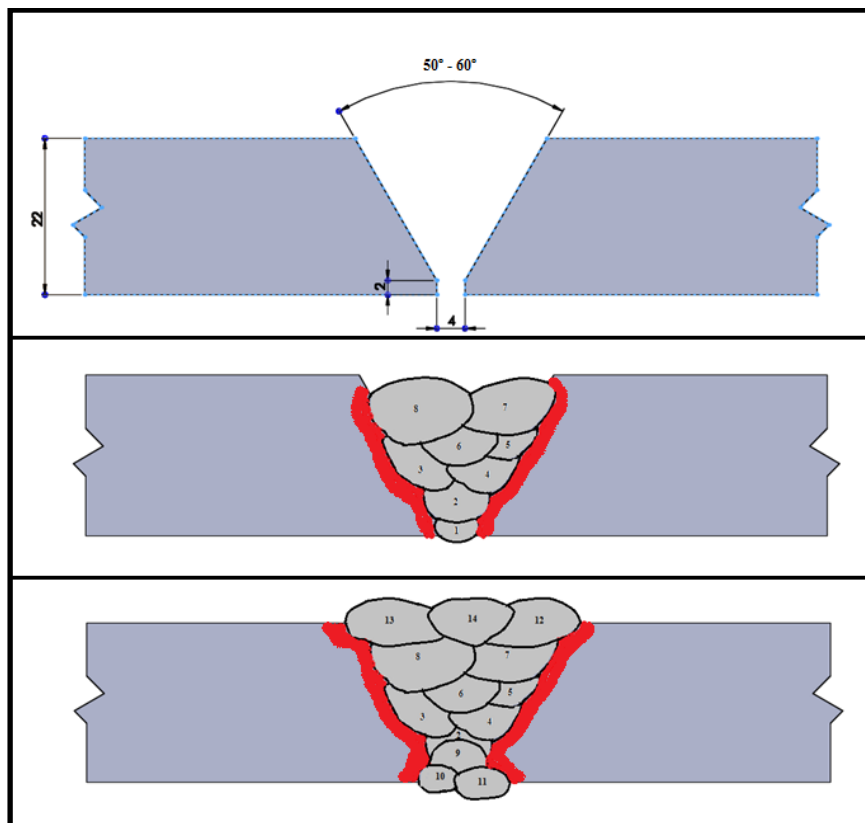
Sequência de cordões na soldadura realizada com fio da FABSHIELD XLR-8
